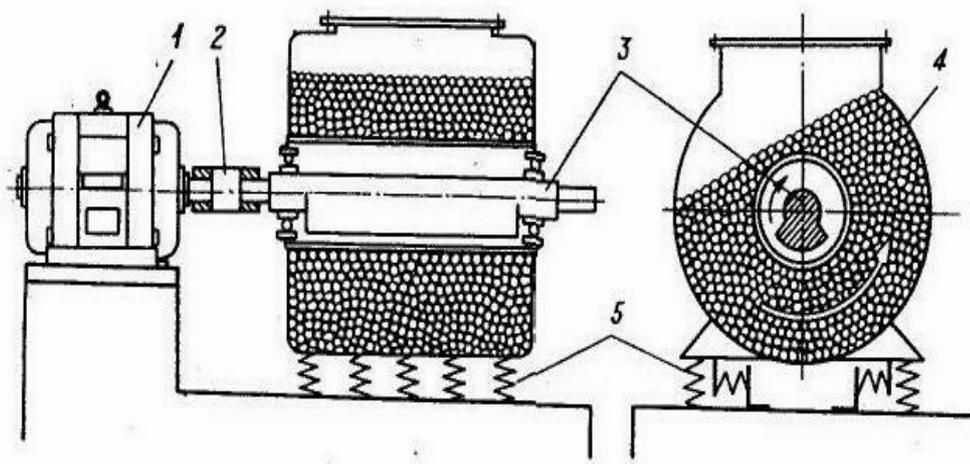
Схема вибромельницы: 1 – электродвигатель; 2 – эластичная муфта; 3 – вал с дебалансом; 4 – корпус; 5 – пружины
